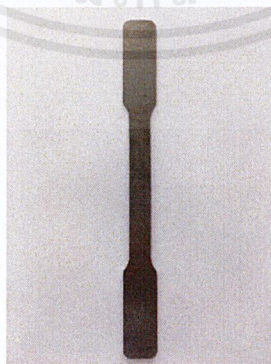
ข เหล็กแผ่นก่อนจะขึ้นรูปเป็นชิ้นงานด้วยเครื่อง Hydraulic pressing machine
